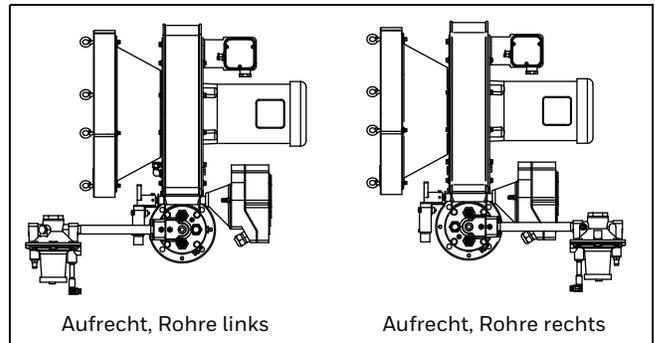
Brennerkonfiguration und gewählte Ausrichtung des Motors
